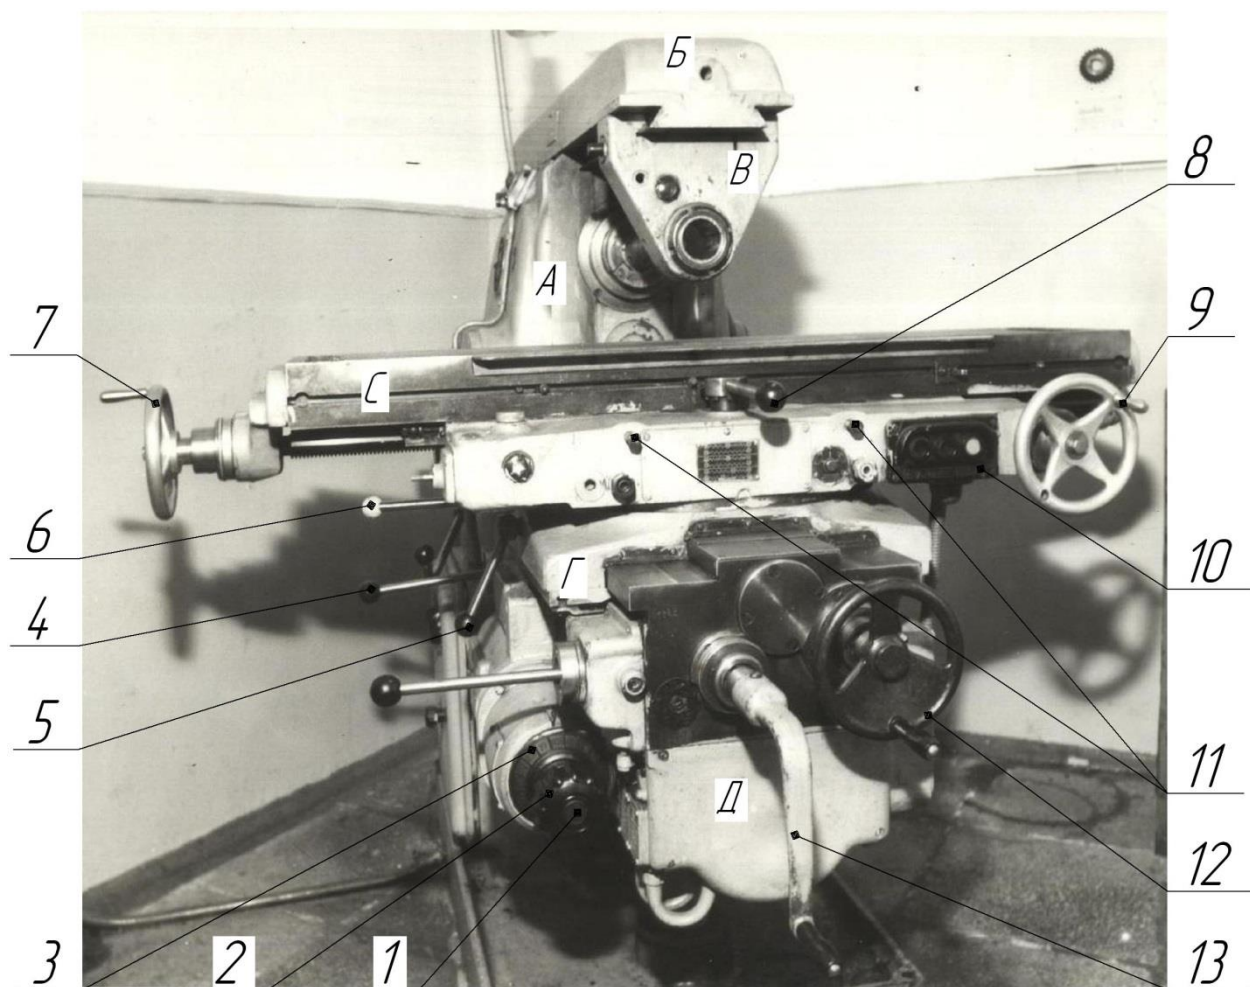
Общий вид станка спереди: А – станина; Б – хобот; В – серьга; С – стол; Г – салазки; Д – консоль; 1 – кнопка; 2 – грибок; 3 – лимб; 4 – рукоятка включения механических подач консоли и салазок; 5 – рукоятка зажима салазок; 6,8 – рукоятка включения механической продольной подачи стола; 7,9 – маховики для ручного перемещения стола; 10 – кнопочная станция; 11 – болты фиксации стола; 12 – маховик ручного перемещения салазок (поперечная подача); 13 – рукоятка ручного перемещения консоли (вертикальная подача)
